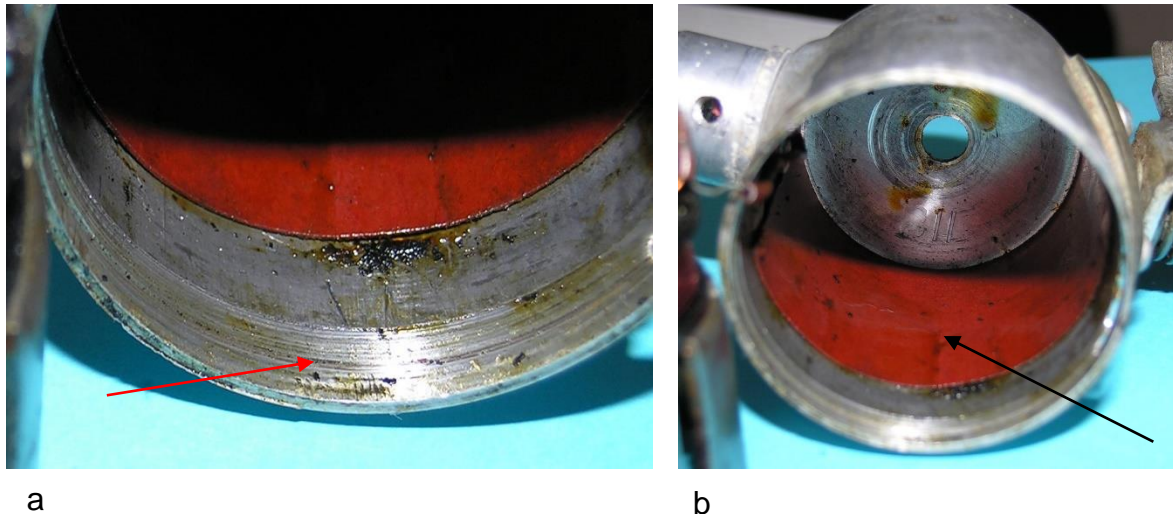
Innenraum des Gehäusetopfes: a) Umlaufende Nut für den Drahtverschluss, b) Großflächige Isolierfolie auf der Gehäuseinnenwand
